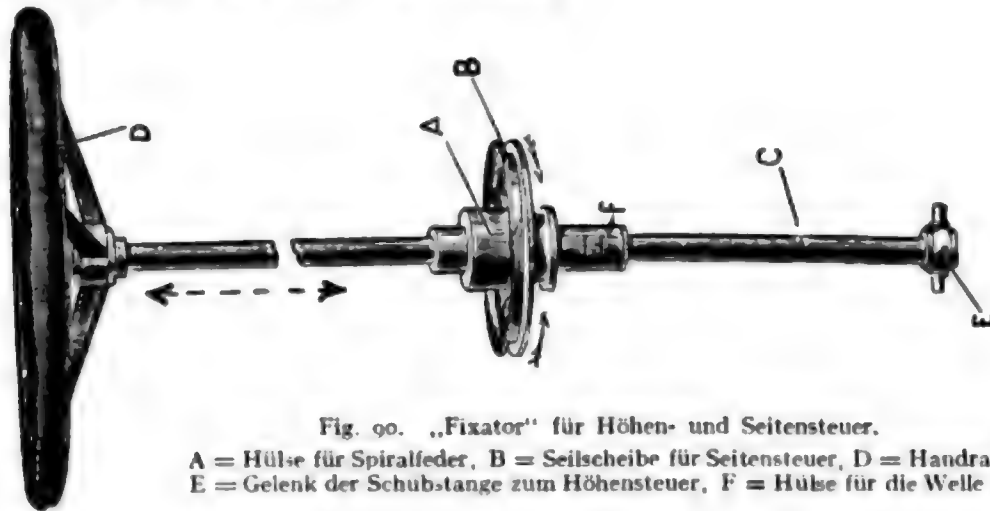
„Fixator“ für Höhen- und Seitensteuer.
